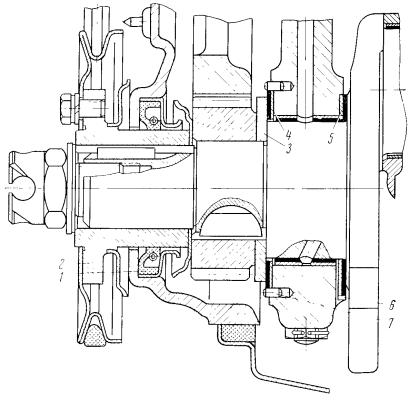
Передний конец коленчатого вала: 1 — сальник; 2 — ступица шкива; 3 — упорная шайба; 4 —передняя шайба: — задняя шайба; 6 — выступ шайбы, 7 — штифт
